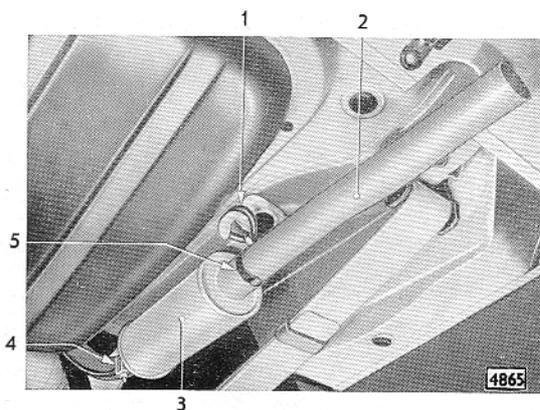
Befestigung und Aufhängung des rechten hinteren Auspuffrohres und -topfes am mittleren Auspuffrohr – in Fahrtrichtung gezeigt
